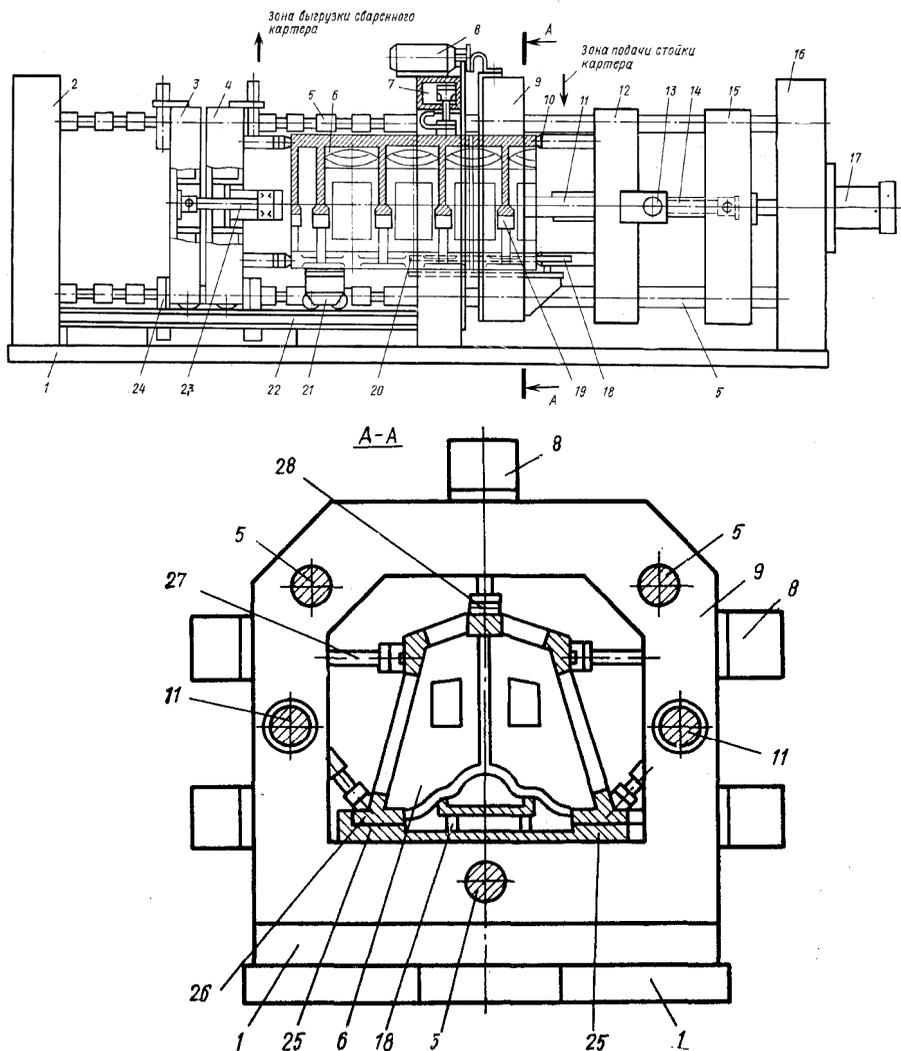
Схема контактной машины для сборки и сварки картера блока дизеля
